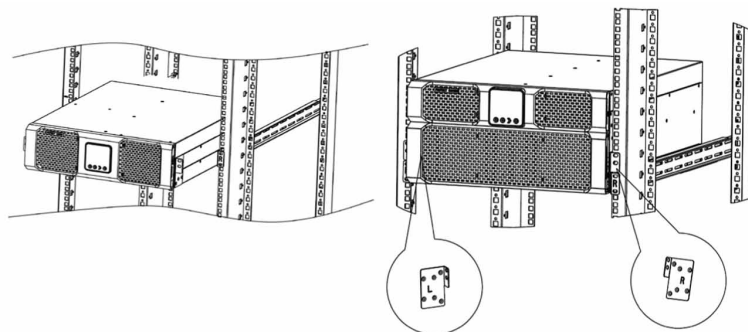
Слева – монтаж устройства Protect D. 6000, справа – устройство Protect D. 10000 с боковыми уголками крепления.
